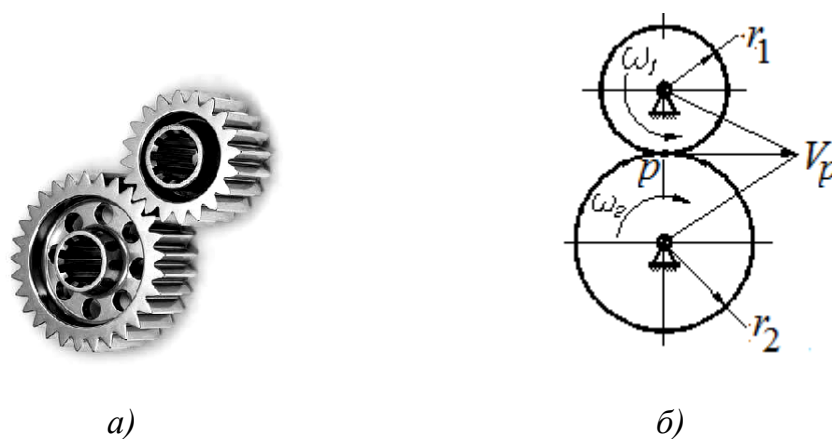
Зубчатая передача: а – общий вид; б – схема
